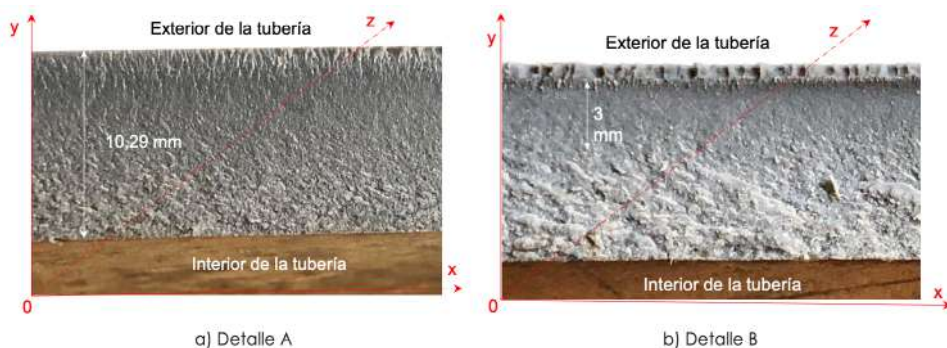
Detalle A y B de las roturas PVC-U DN-200
